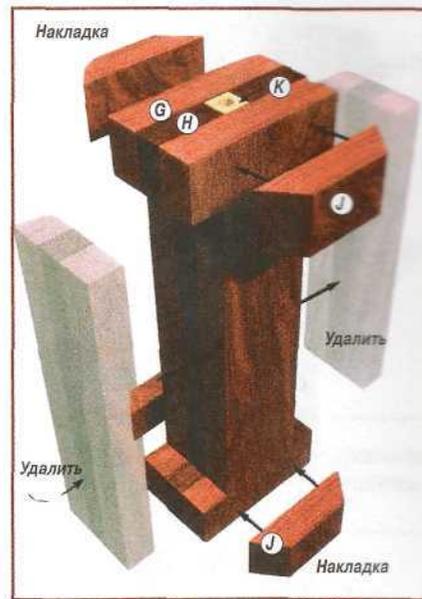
Клееный блок-заготовка для ножки. Чтобы облегчить обработку на токарном станке, фрагменты, указанные стрелками, вырезают на ленточной пиле.
